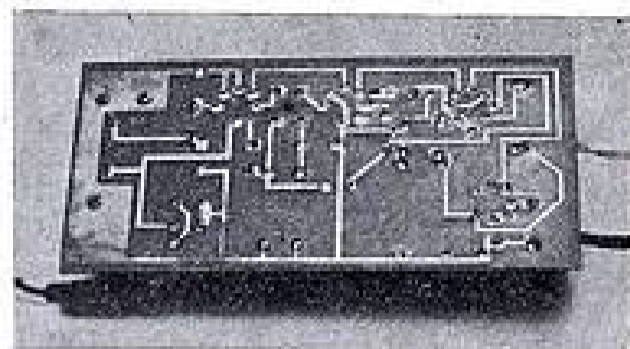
Le dessous du panneau. On voit le circuit imprimé et toutes les connexions soudées.
